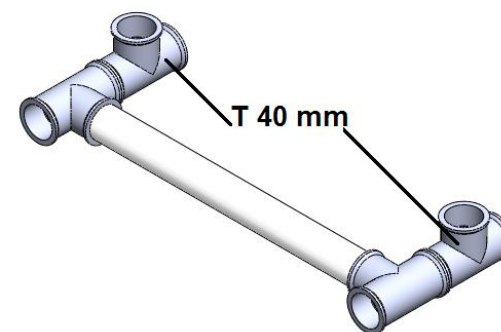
Montagem dos módulos – Módulo 4 – Passo 3
